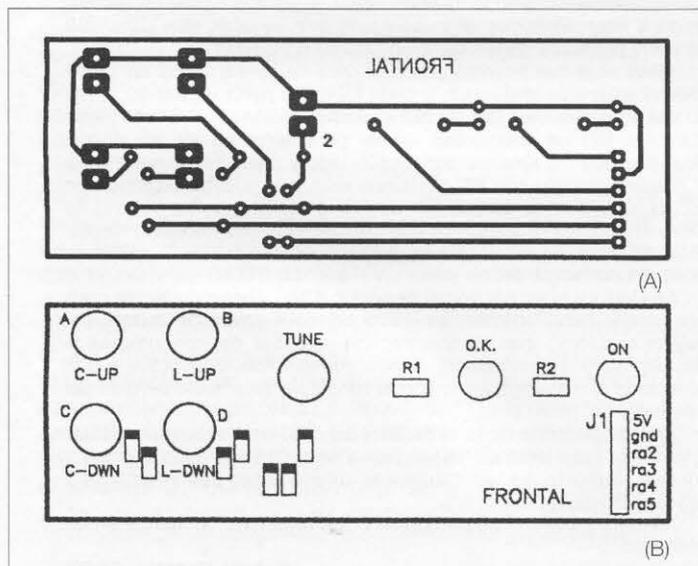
Plantilla de la placa para el panel frontal (A) y disposición de componentes (B).
